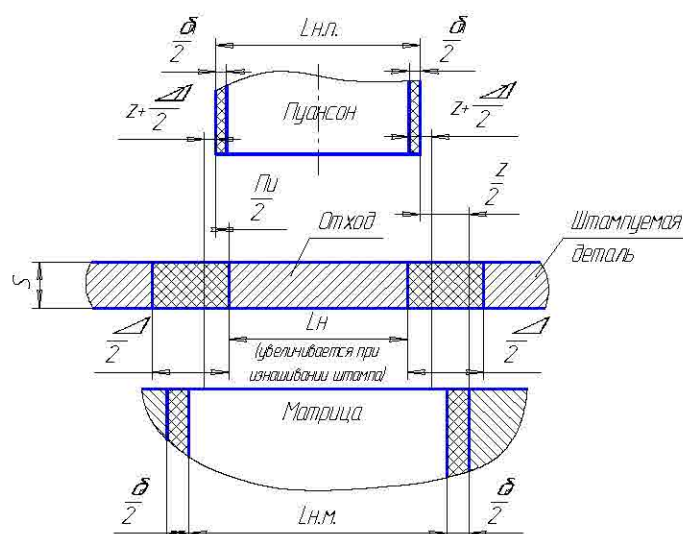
Схема розмірів і полів допусків
